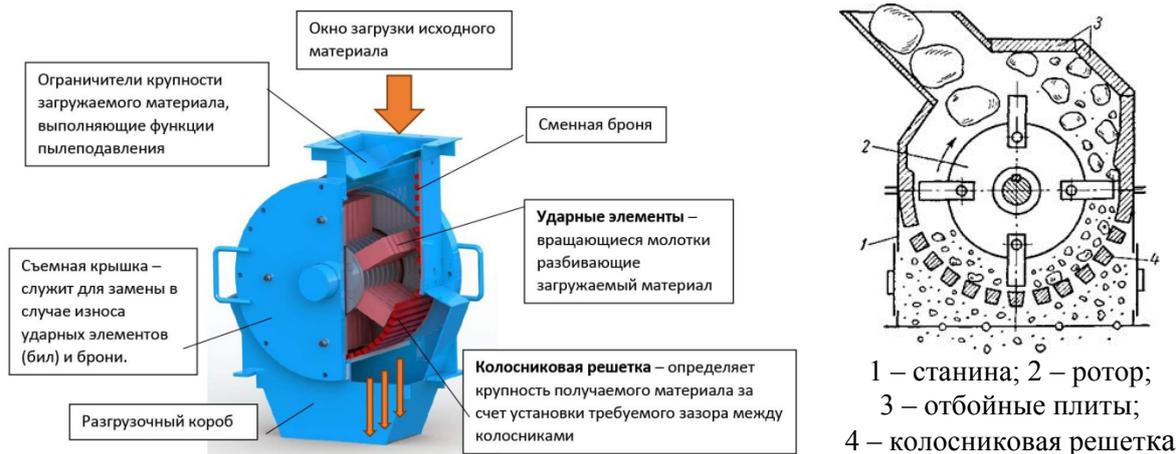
Механизм молотковой дробилки и конструктивная схема молотковой дробилки
